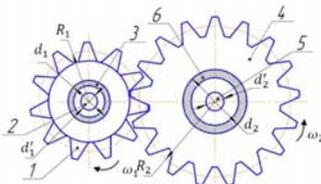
Зубчатая передача с составными кольцами и шестерней, включающая амортизаторы втулки
